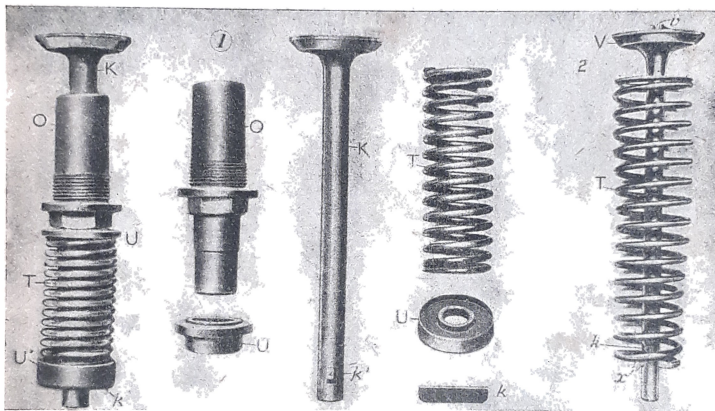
Valvole di scappamento, guide, molle, ecc.
